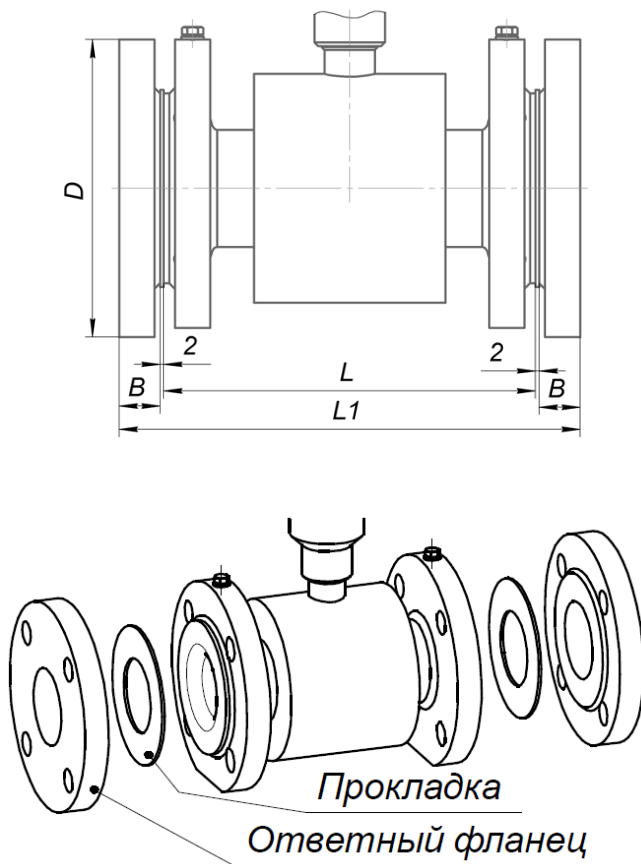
Габаритные размеры сборки расходомера вместе с ответными фланцами и прокладками (без колец заземления).
